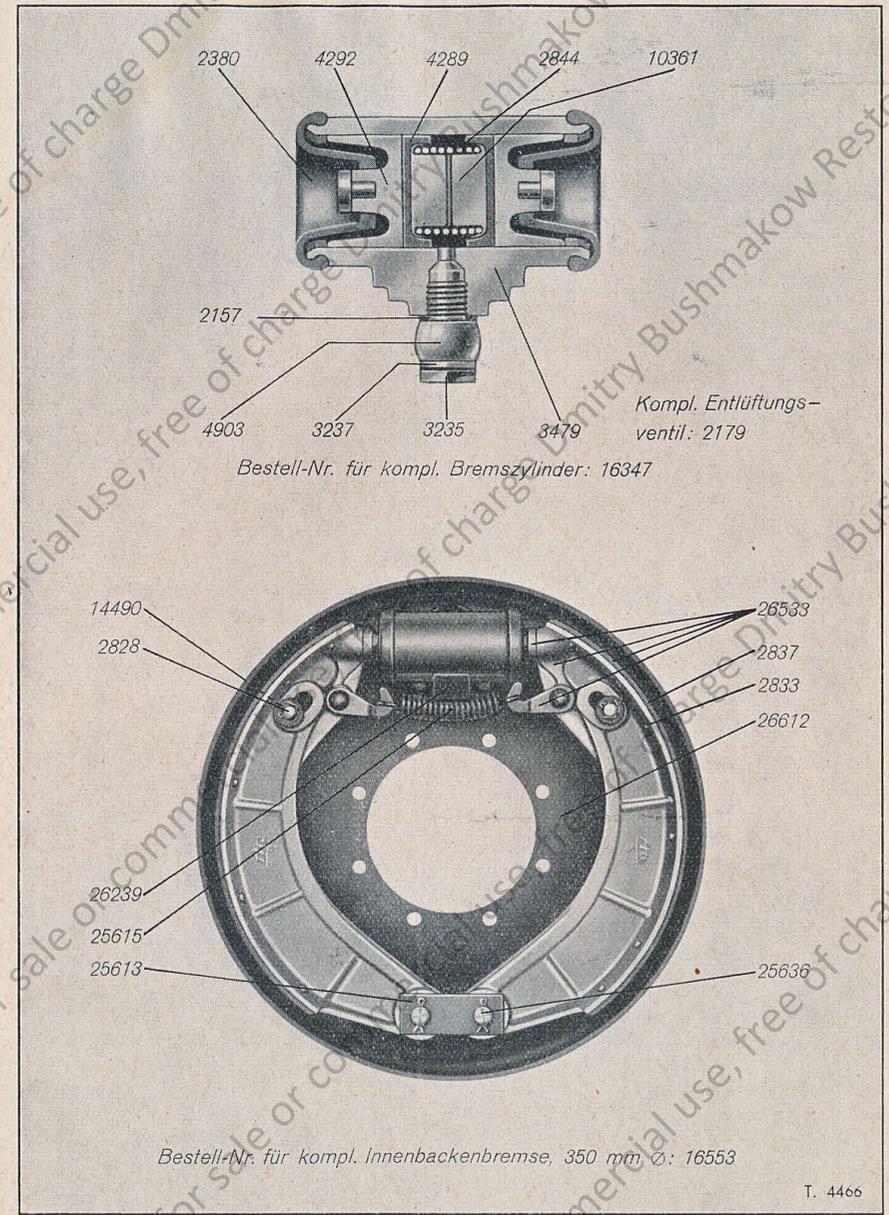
Bezeichnung der Einzelteile siehe Seite 26.
